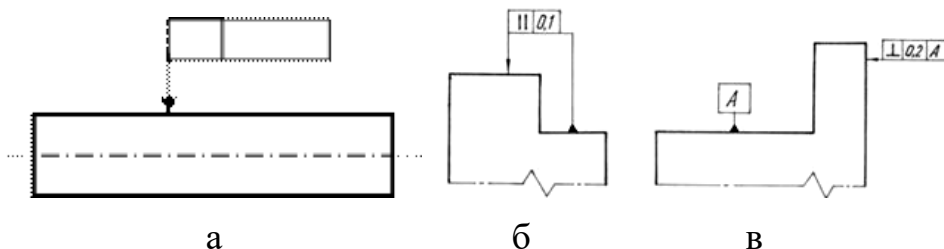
Обозначение допусков формы и расположения поверхностей.
